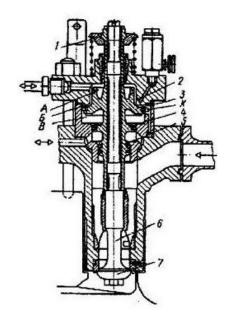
Воздухораспределитель двигателя Зульцер RTA72U ведущая шестерня, 2- кулак, 3- реверсивный поршень, 4- ролик, 5- управляющий клапан, 6- вал, 7 – ведущая шестерня, 8- крышка шестеренного привода, АА- штуцер подвода пускового воздуха, АL- пусковой воздух к управляющим клапанам, EL- вентиляция (сброс давления), LA- пусковой воздух от пневматического логического элемента для хода вперед, LB- пусковой воздух от пневматического логического элемента для хода назад, LC-пусковой воздух к отключающему клапану, LD- Пусковой воздух к пусковым клапанам, OB- отверстие подачи смазки, при открытии главного пускового клапана воздух заполняет
